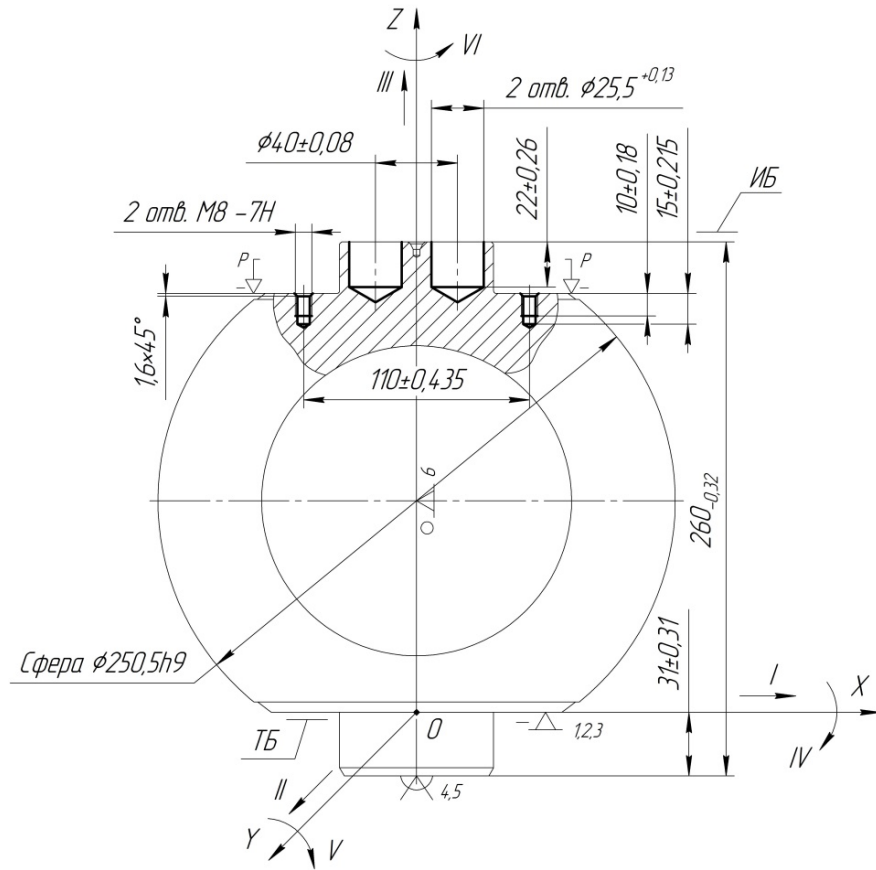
Базування заготовки на операції 050. Схема №1
